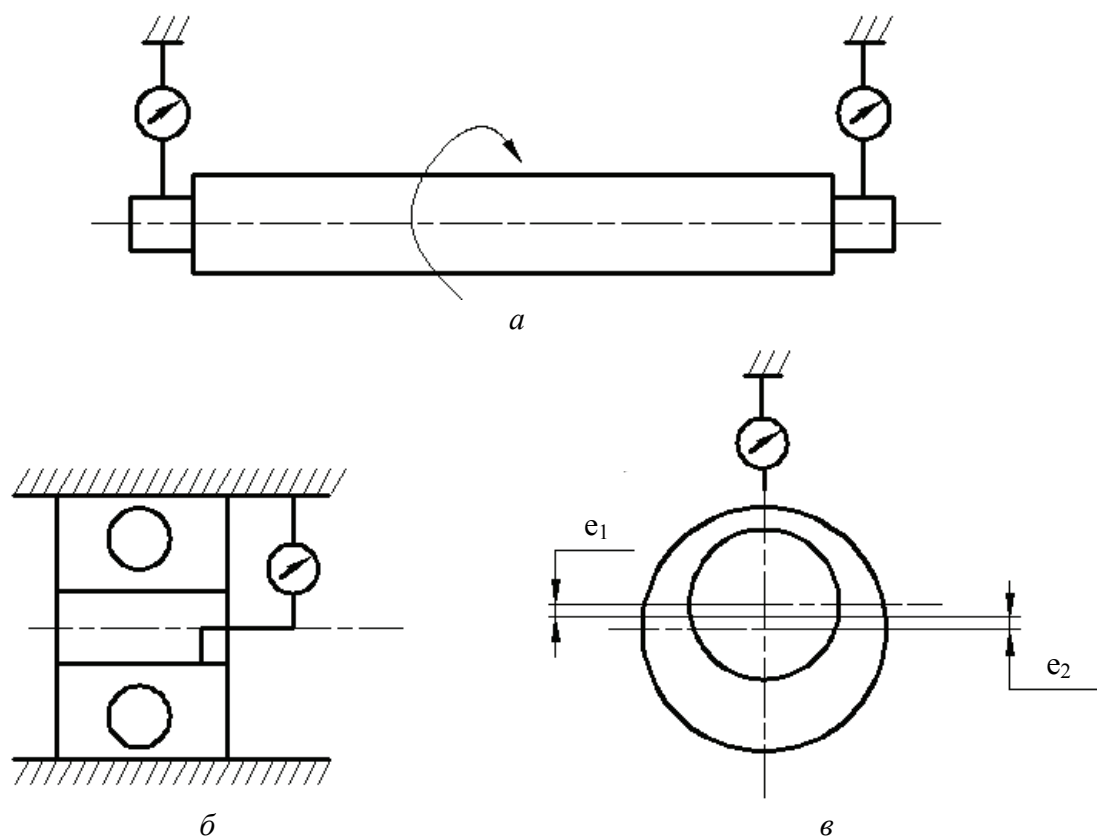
Схема сборки вала на опорах качения: *a* – измерение эксцентриситета шеек вала; *б* – измерение эксцентриситета внутреннего кольца подшипника; *в* – расположение эксцентриситетов шейки вала и внутреннего кольца подшипника
